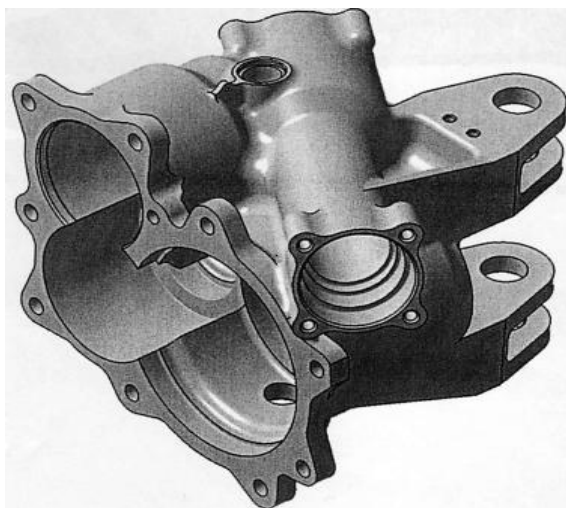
Оптимизированная модель корпуса из сплава ВАЛ20
